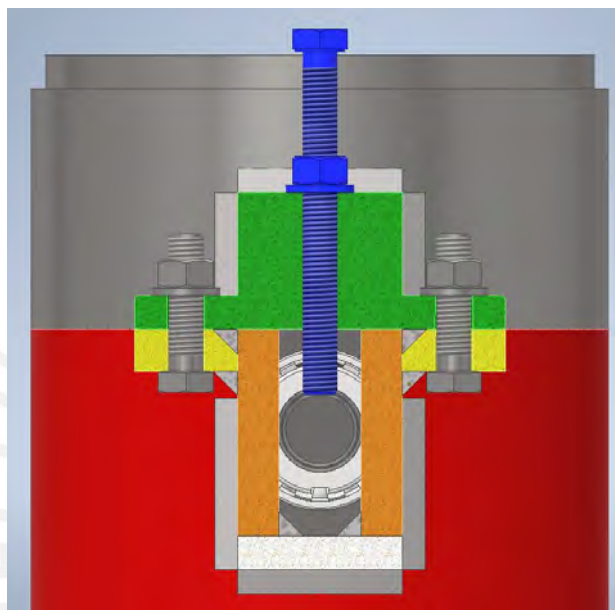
Unión atornillada de apoyo del eje de rodillos.
